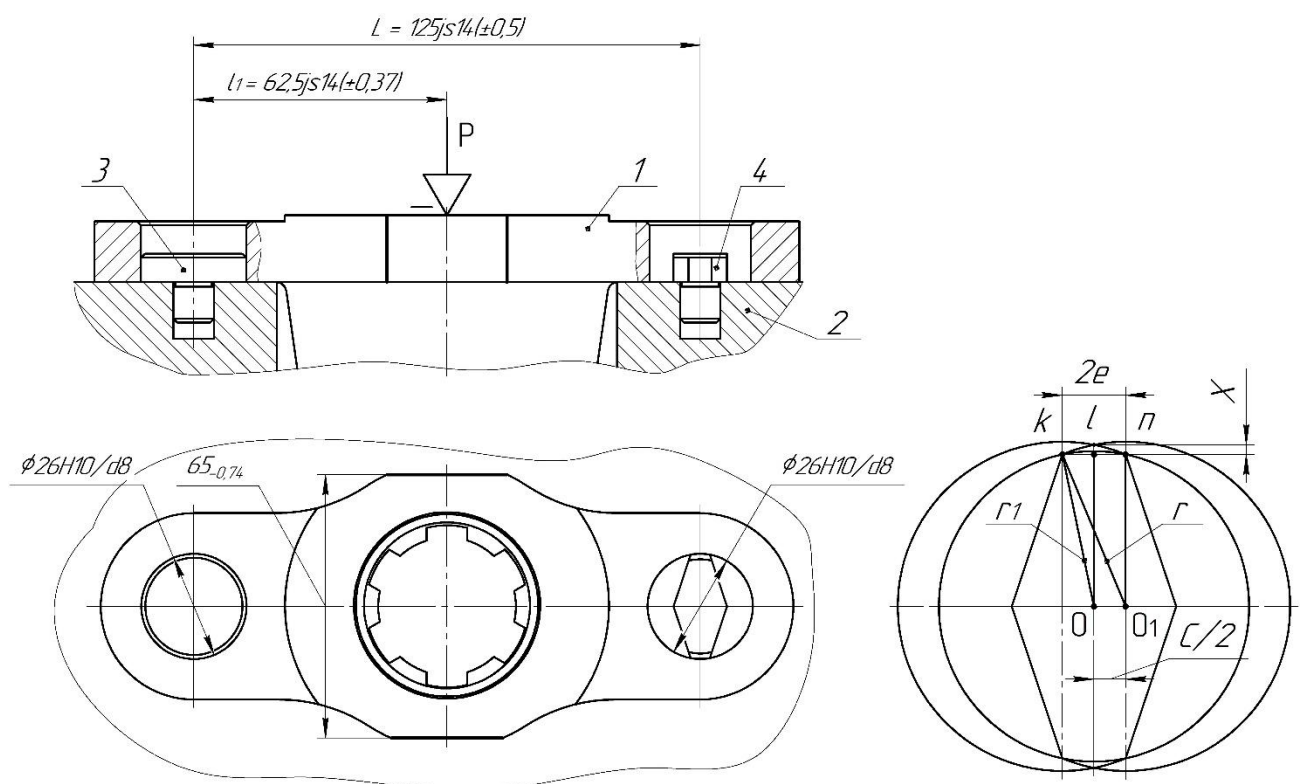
Схема установки заготовки на пальці: 1 – заготовка; 2 – площина пристрою; 3 – палець циліндричний; 4 – палець ромбічний (зрізаний)
